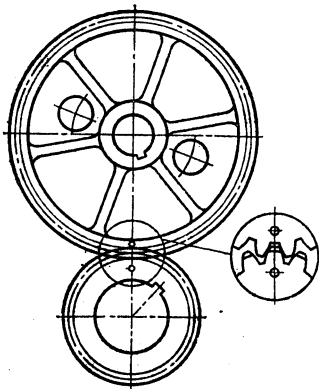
Положение меток на зубчатых колесах при установке фаз газораспределения
